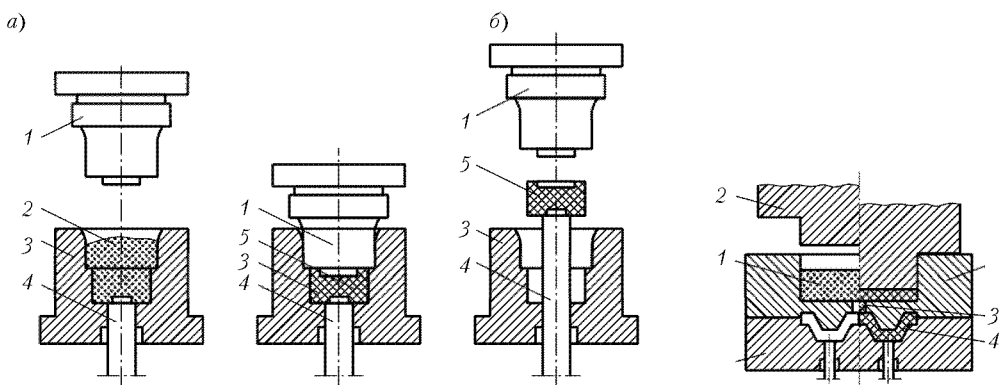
Схемы: а — прямого (компрессионного) и б — литьевого прессования: 1 — пуансон; 2 — матрица; 3 — пресс-материал; 4 — изделие; 5 — загрузочная камера; 6 — литниковая система
